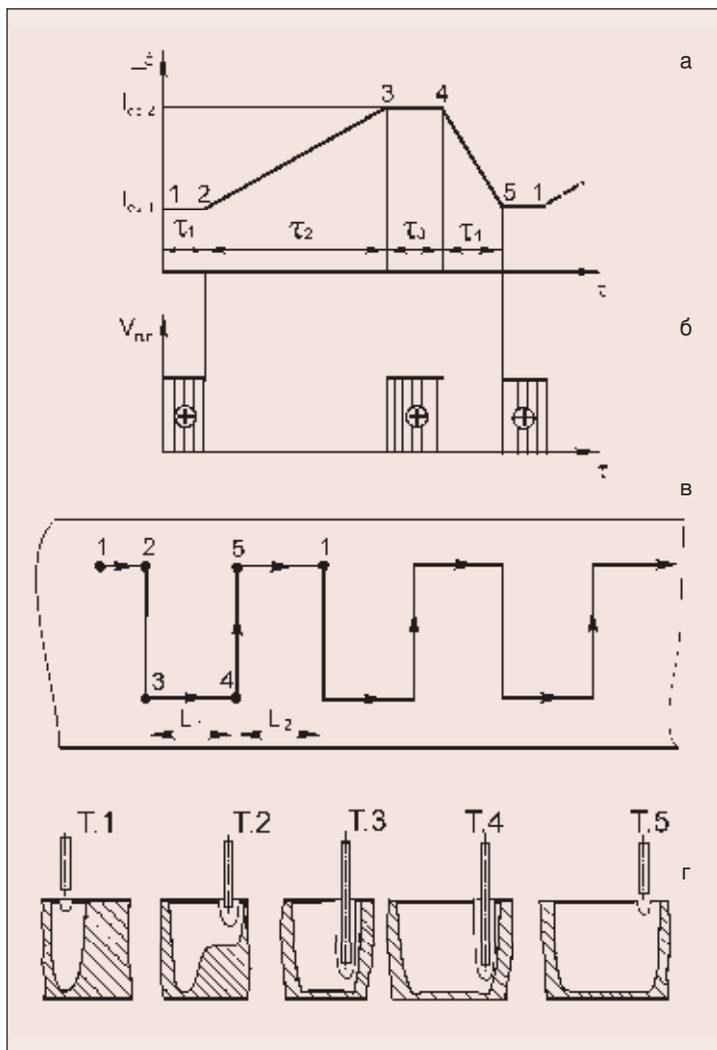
Способ сварки с ППР по схеме IV: а — характер изменения силы сварочного тока; б — график перемещения сварочной головки; в — характер перемещения дуги в плоскости свариваемых кромок; г — кинетика проплавления основного металла
